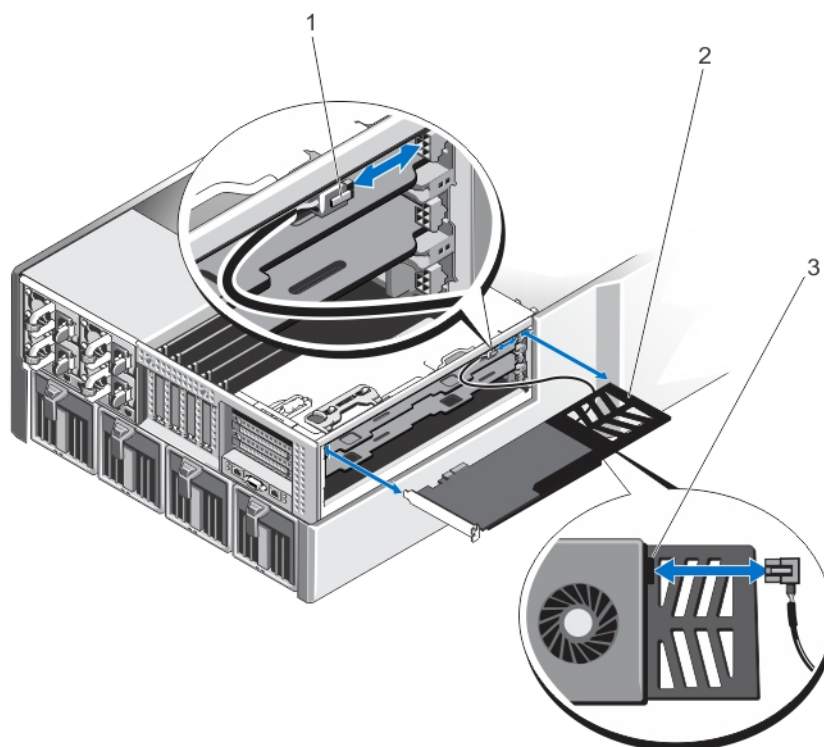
Retrait et installation du câble d'alimentation sur la carte d'extension
